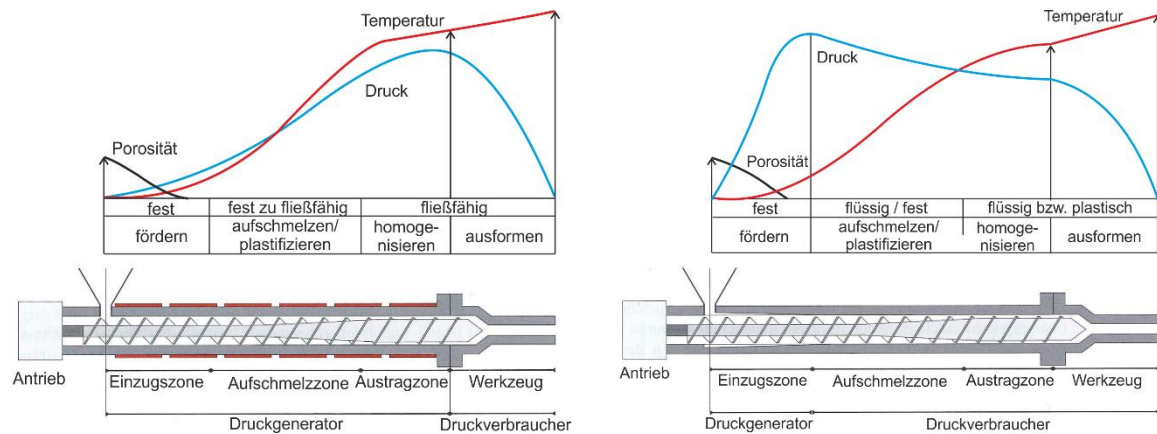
Druckaufbau im Einschneckenextruder: Glattrohretruder (links), Nutbushenextruder (rechts) [33]
